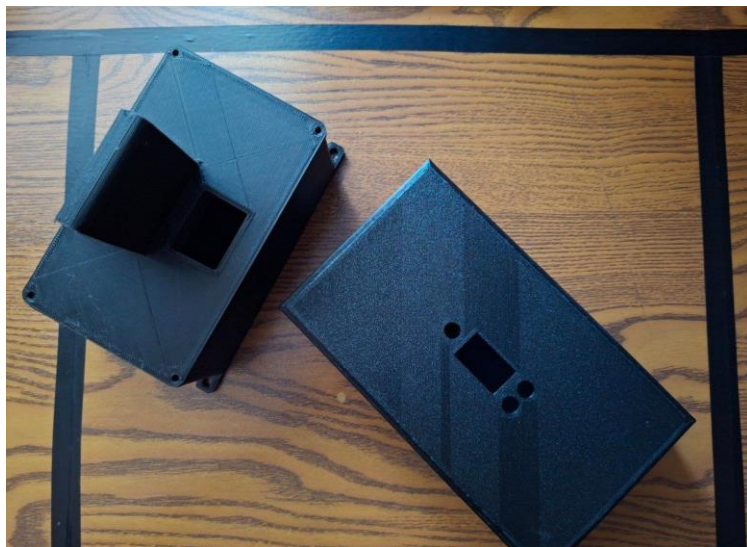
Загальний вигляд виконаного корпусу
